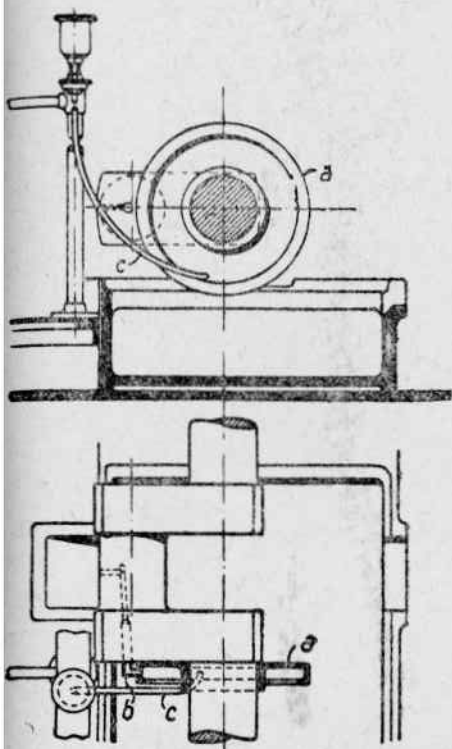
Центробежное смазывающее приспособление для кривошипного вала. *a*—кольцо для центробежной смазки, *b*—угловая трубка, *c*—трубка, подводящая масло.
